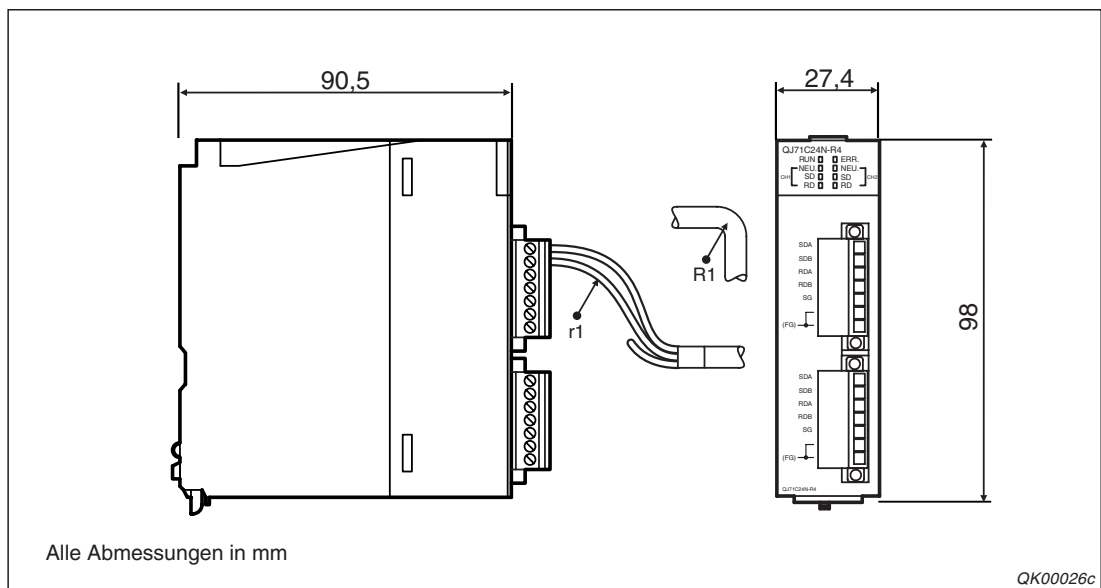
Abmessungen des Moduls QJ71C24N-R4
